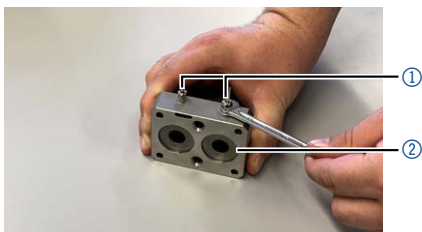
Entfernen der Verschraubungen der Hinterkolbenspülung
